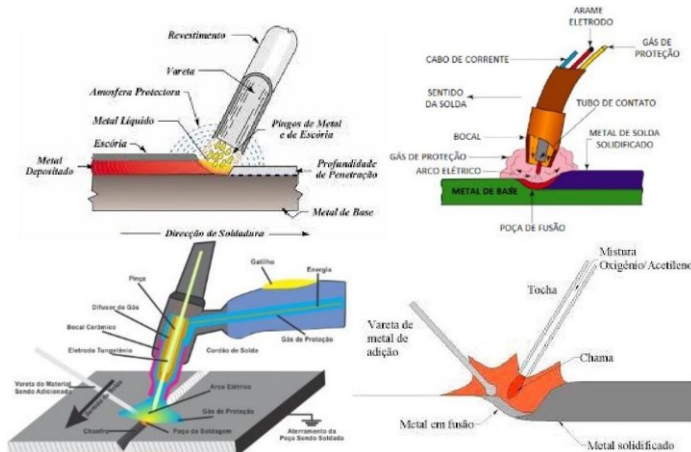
Os vários processos de soldadura: eletrodo revestido (SER) / MIG-MAG / TIG / Soldo-brasagem
